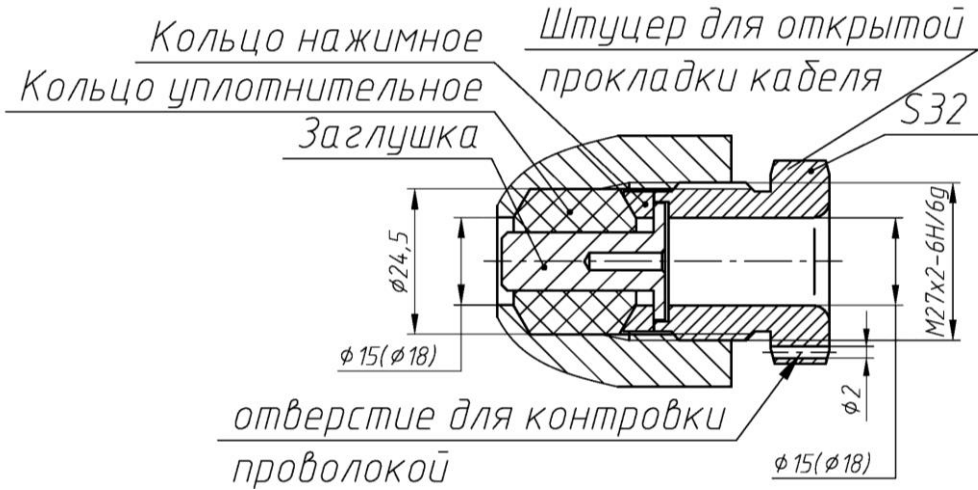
Габаритный чертёж блока датчика извещателей ЕхИО102-1В моделей 03 с элементами взрывозащиты. Пример маркировки взрывозащиты см в п. 6.1
